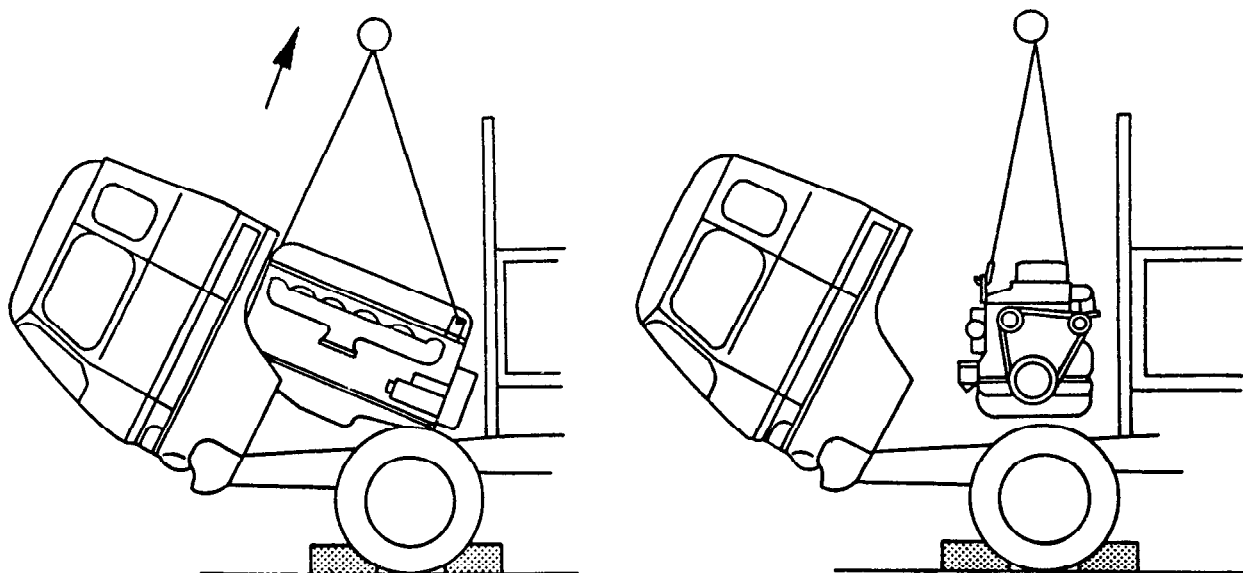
Desmontaje del motor de un vehículo con cabina de inclinación
